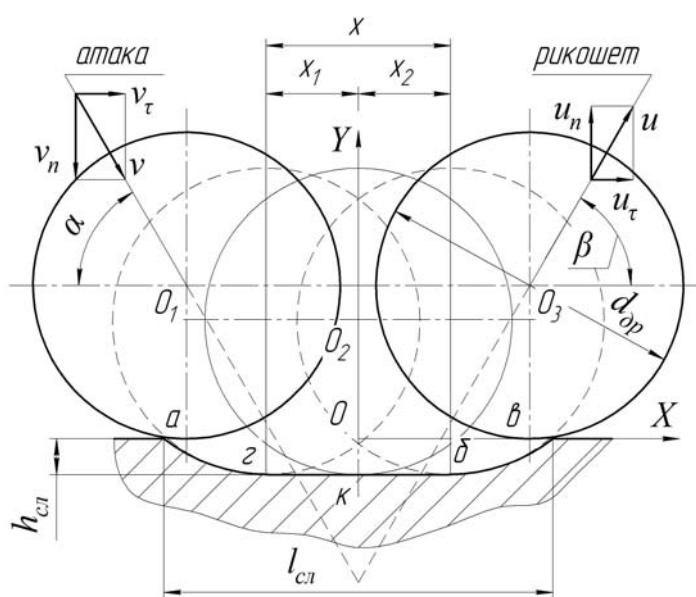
Схема взаємодії дробинки з металевою поверхнею
